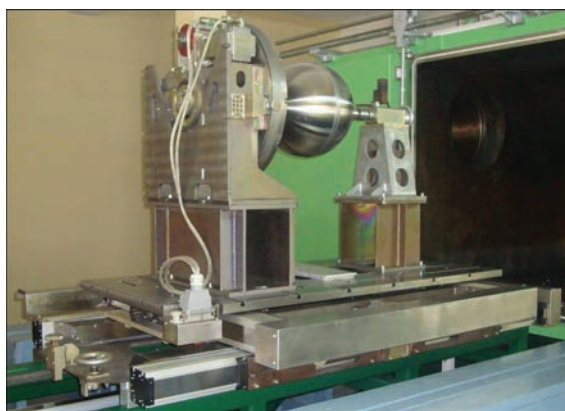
Двухкоординатный рабочий стол среднегабаритной установки с установленными на специальные подставки сварочным манипулятором (вращателем) и задней бабкой
